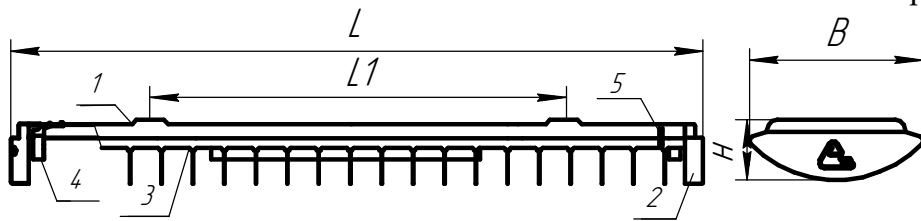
1. Корпус в сборе; 2. Крышка; 3. Решетка;
